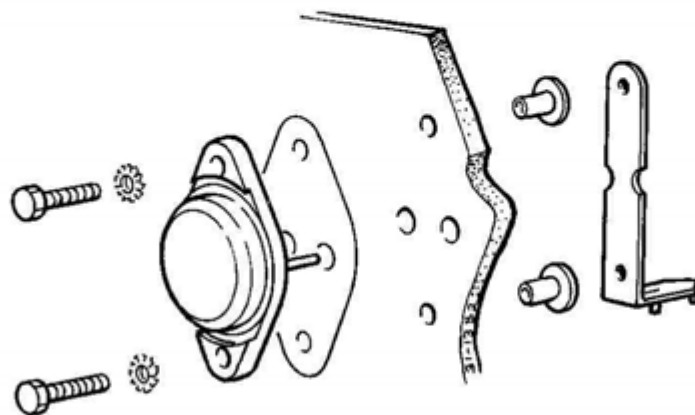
Montering av slutt-transistor, husk silikonfett på begge sider av glimmerskiven.
